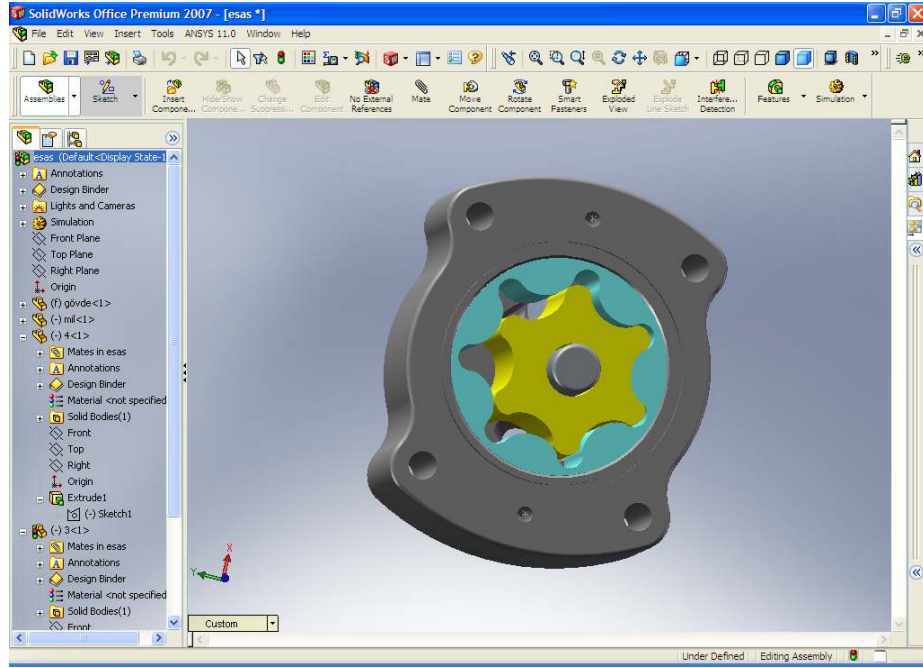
1156-1157 gerotor dişli takımı.
